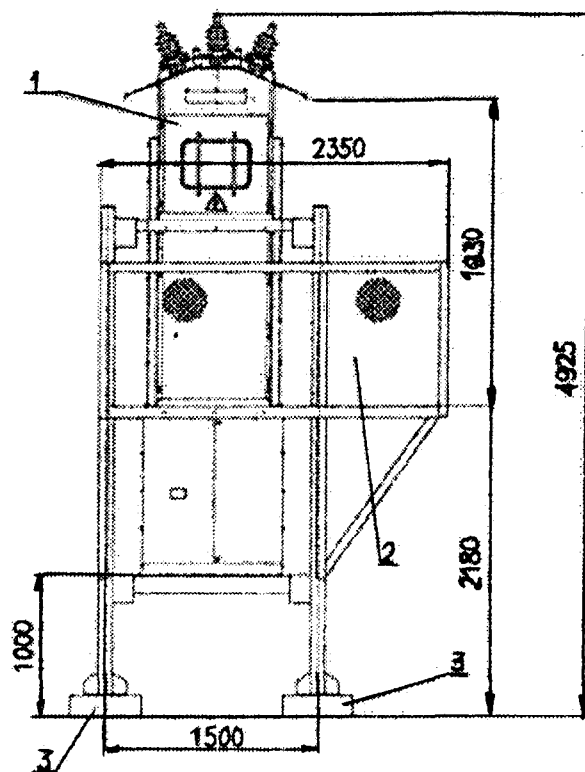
Общий вид и габаритные размеры устройства К-123
